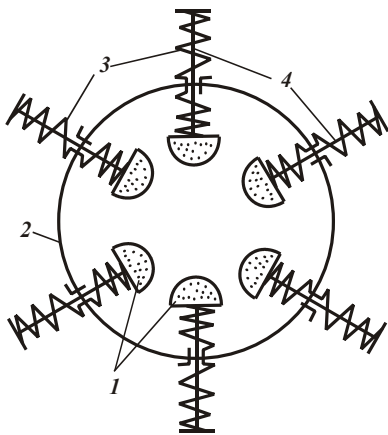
Инструмент для шлифования наружных поверхностей: 1 - шлифовальный брусок; 2 - корпус цилиндрический; 3 - пружина; 4 - штырь.
